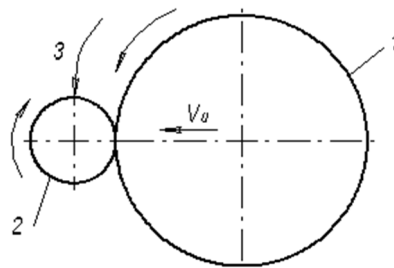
Схема зустрічного шліфування: 1–електрод-інструмент; 2–заготовка; 3–сопло поливу рідиною; V_d – швидкість подачі інструмента
